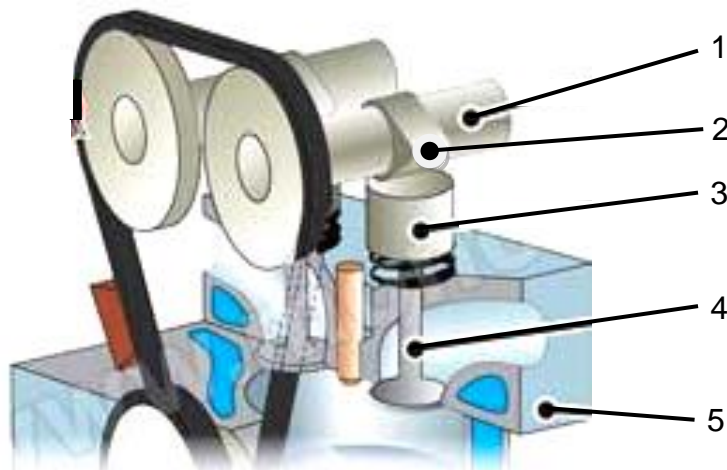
Головка блоку циліндрів з елементами газорозподільного механізму: 1 – розподільний вал; 2 – кулачок розподільного вала; 3 – штовхач; 4 – клапан; 5 – головка блоку циліндрів
